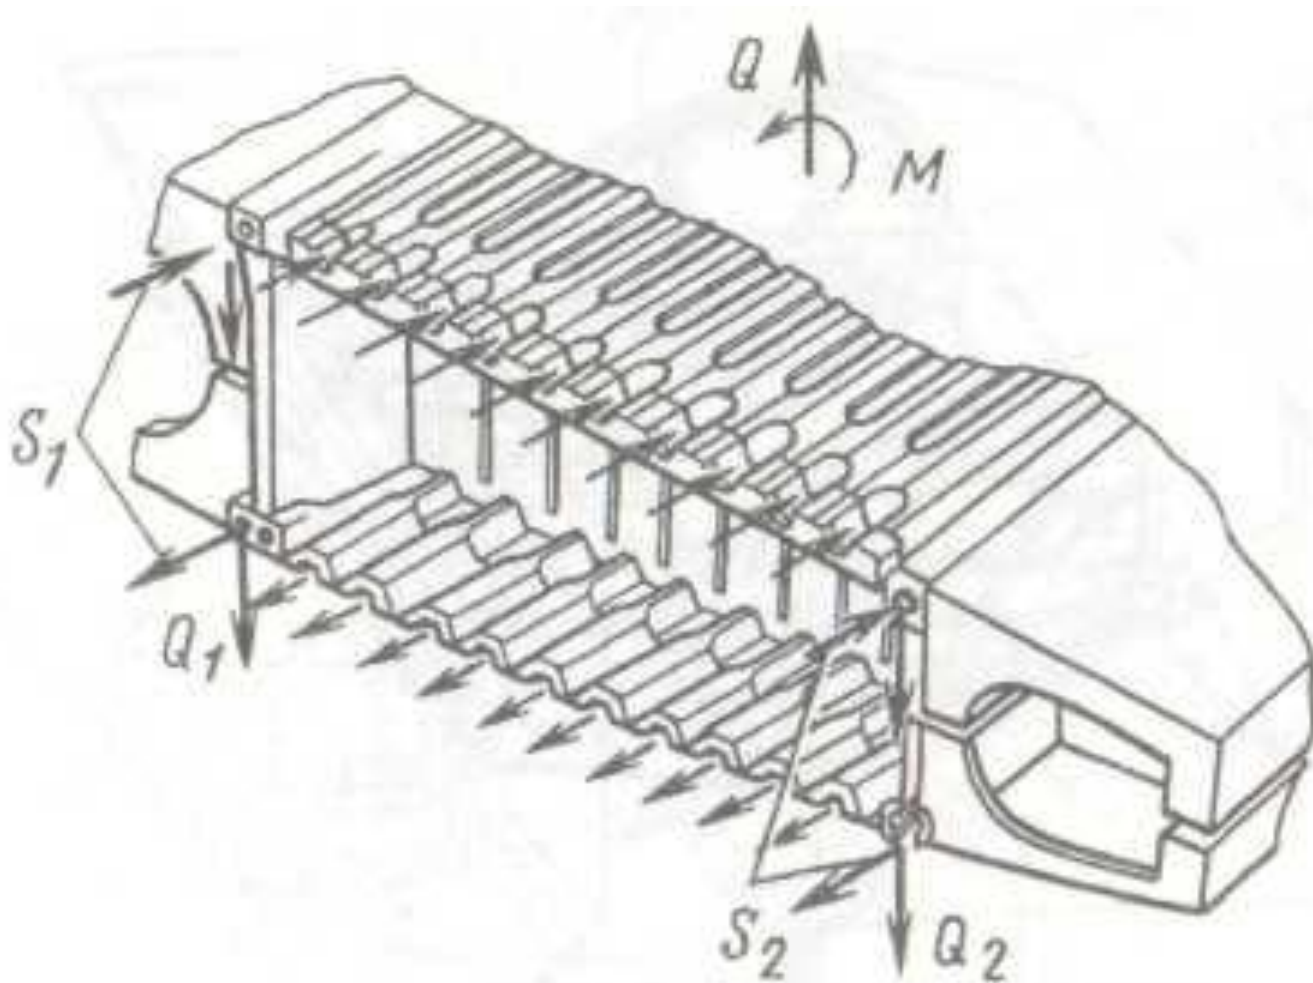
Вариант конструкции стыкового соединения контурного узла кессонного крыла
